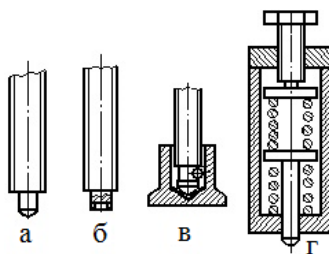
Конструкции винтов с различной опорной поверхностью:
